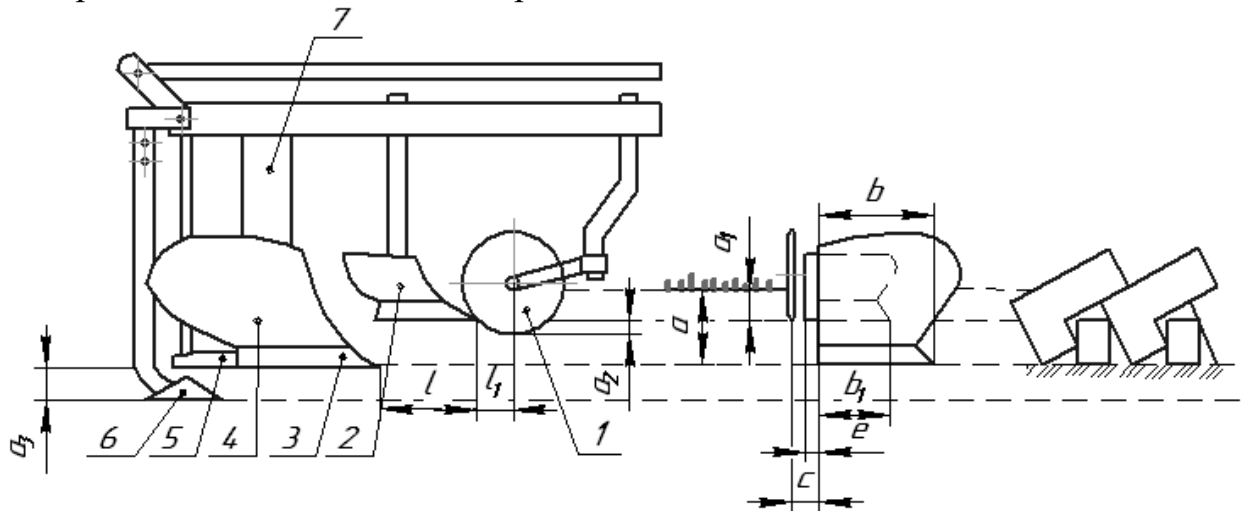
Схема расстановки рабочих органов плуга
